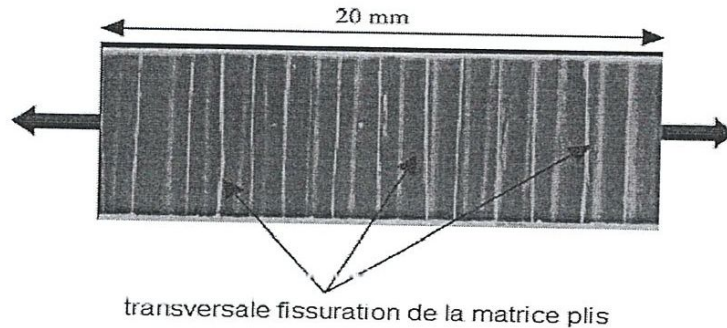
Vue en plan montrant la fissuration transversale dans les 90 plis de GFRP [90/0] s stratifié.
